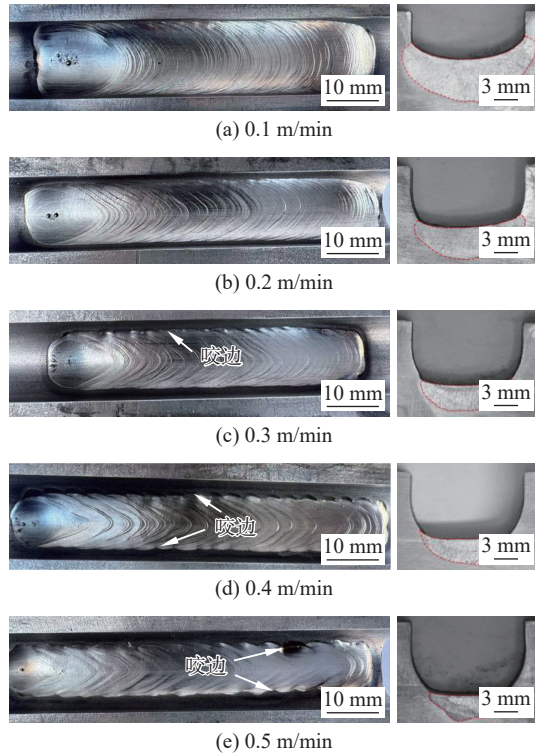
不同焊接速度焊缝表面成形及截面形貌
